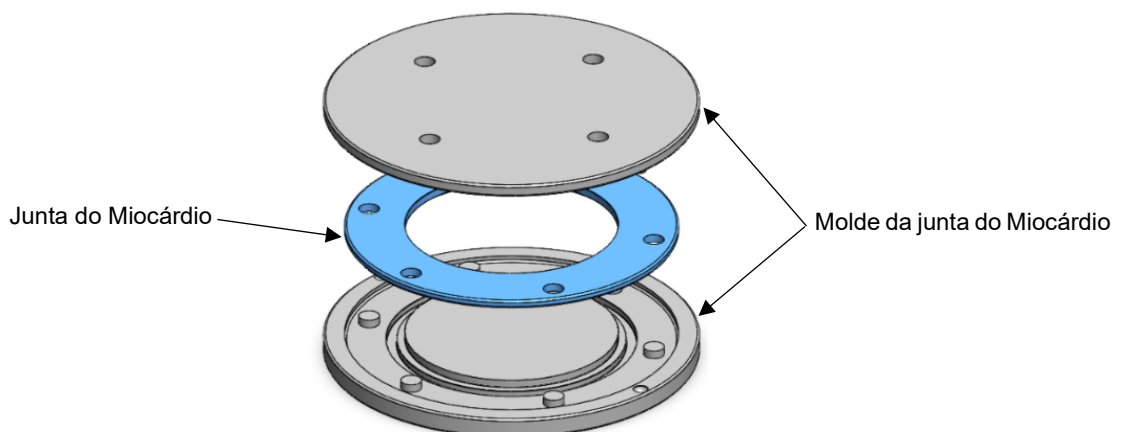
Vista explodida do modelo digital do conjunto Moldes e Junta do Miocárdio. Imagem do autor.
